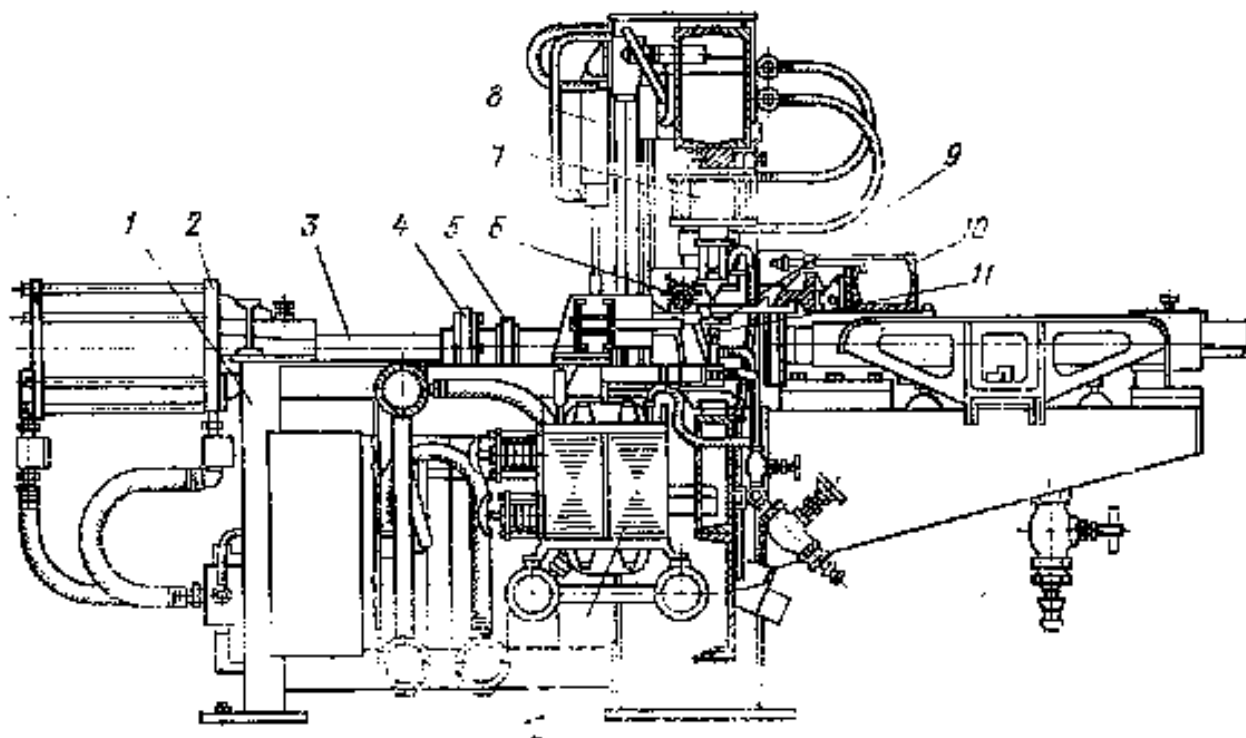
Многоточечная сварочная машина АТМС-14Х75-7-2
